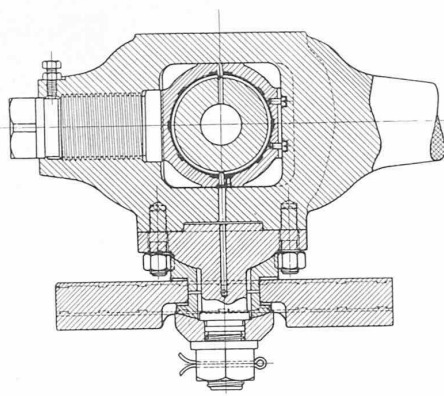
Kreuzkopf einer Sulzer-Schiffmaschine. — Masstab etwa 1 : 12.
